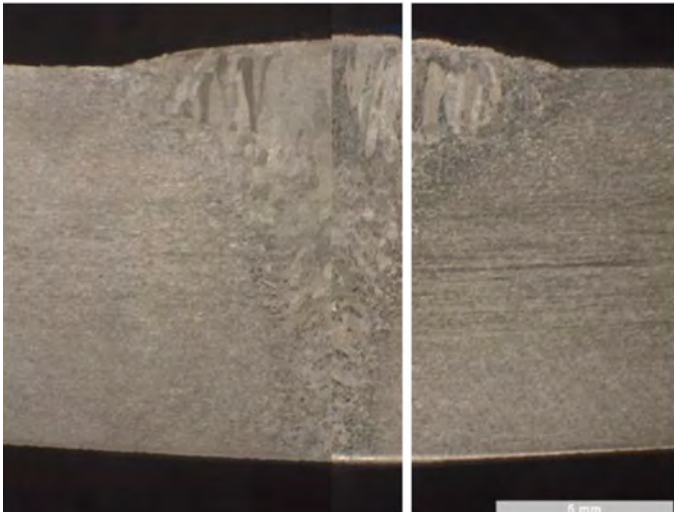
Macro de la soldadura. Izq Exaton 22.8.3LSi Drch. Exaton 22.8.3L
